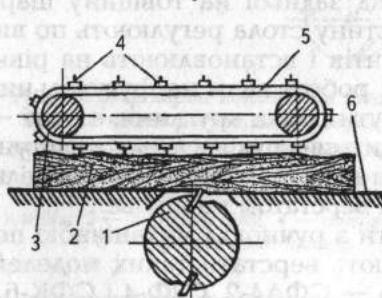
Схема конвеєрного механізму фугувального верстата СФА6-2:
